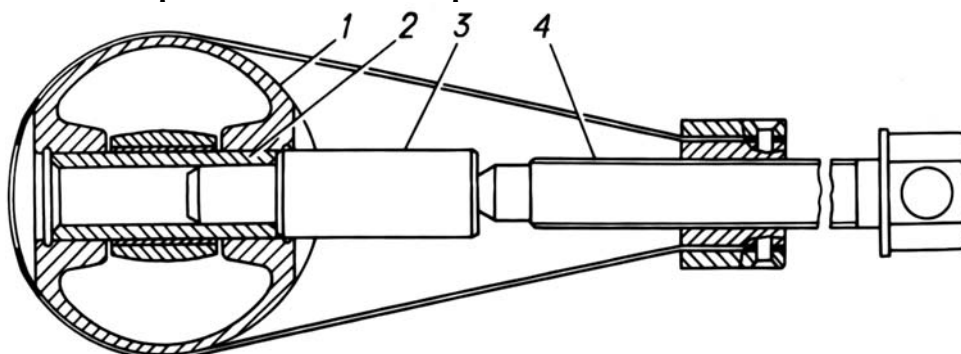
Выпрессовка поршневого пальца из поршня при помощи приспособления: 1 - поршень; 2 - поршневой палец; 3 - оправка; 4 –винт
